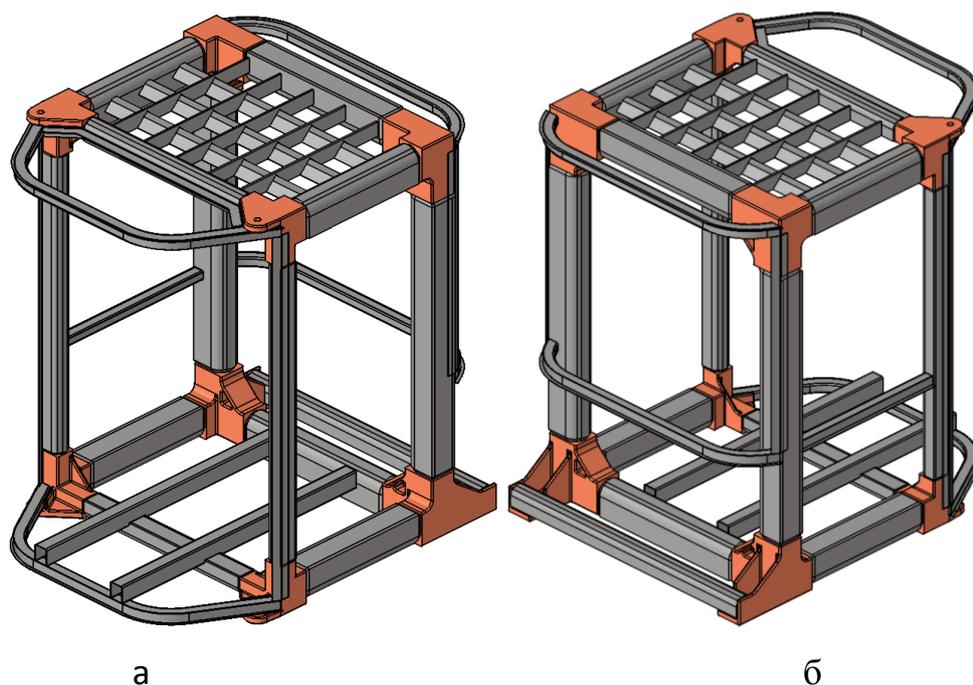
Каркас кабины из алюминиевого сплава: а – вид спереди; б – вид сзади
